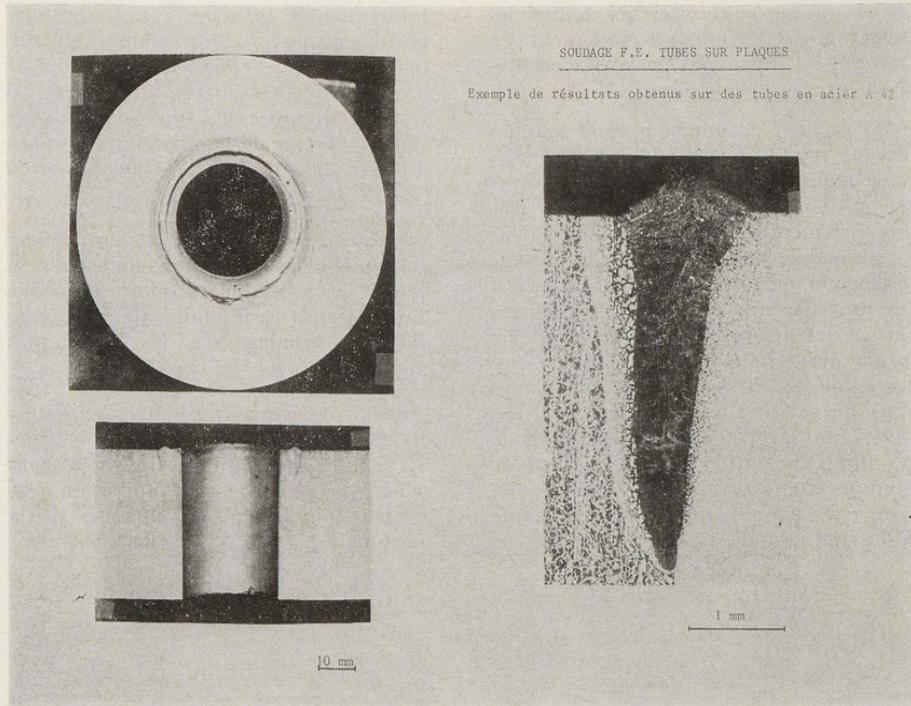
Soudage par faisceau d'électrons de tubes sur plaques - exemple de résultats obtenus sur des tubes en acier A 42.
